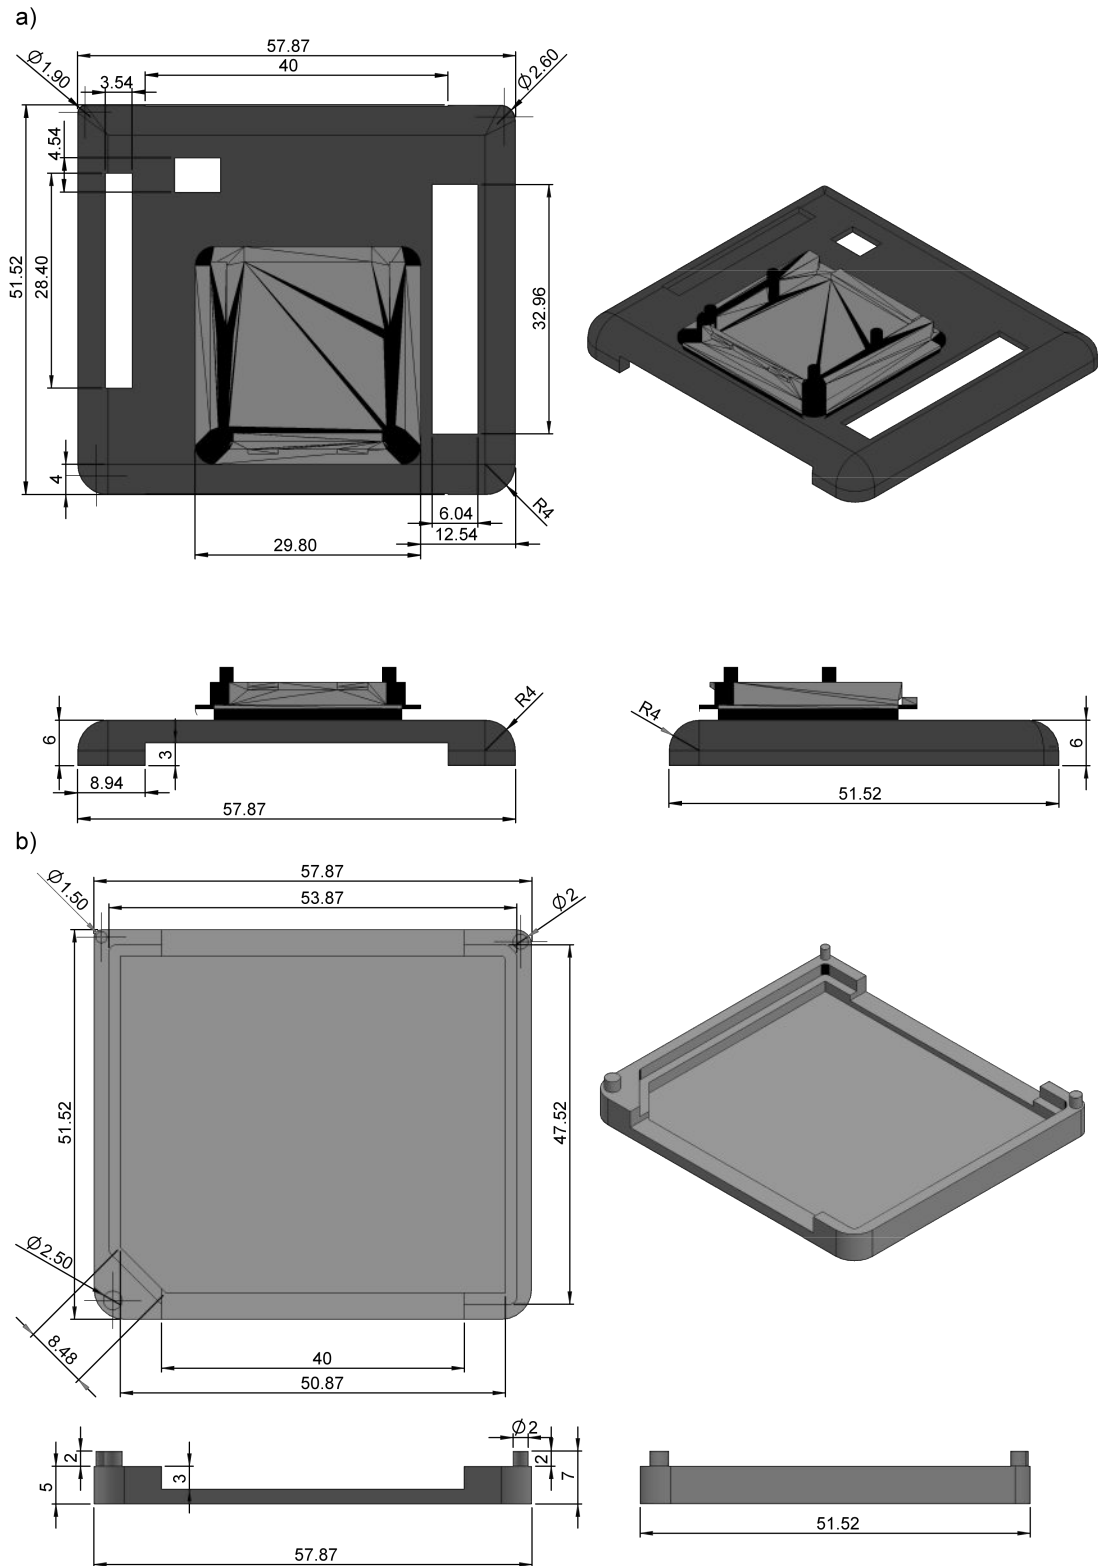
Diseño de carcasa para protección de tarjeta controladora de LEDs. a) Parte superior de carcasa para PCB. Se puede observar cómo está unida a la base inferior de la carcasa para la cámara. b) Parte inferior de carcasa para PCB, esta figura deja entrever cómo se une a la parte superior y la apertura para disipación del calor.
